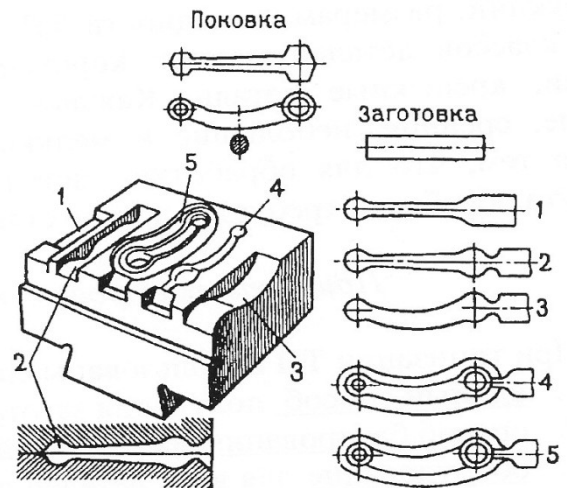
Многоручьевой штамп для получения заготовки изогнутого рычага
